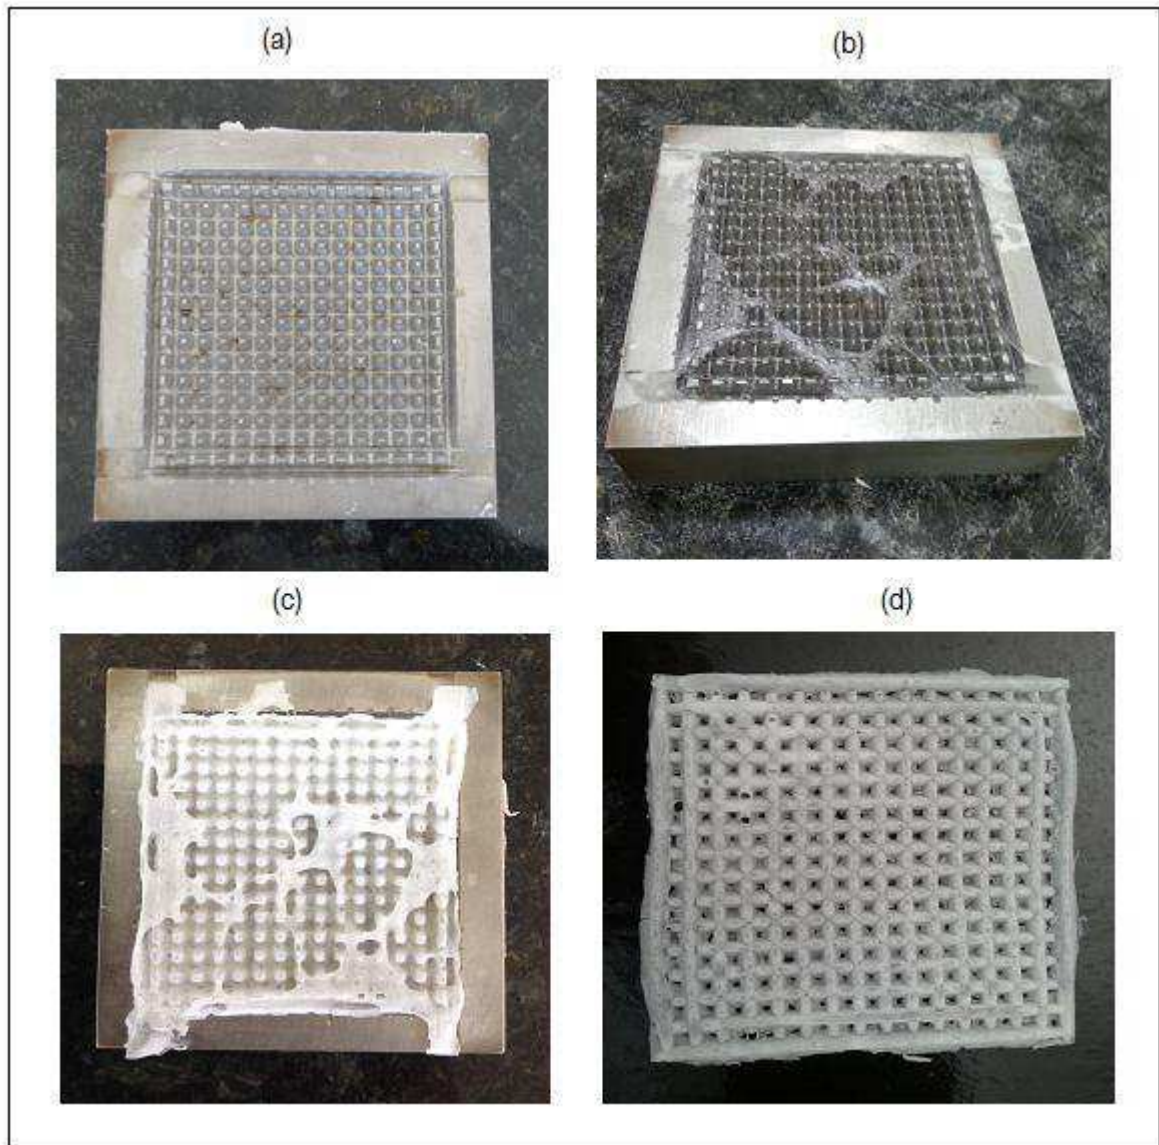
Confeção da tela de PCL, (a) Molde de Ferro, (b) Distribuição do PCL + solvente, (c) Secagem da tela no molde, (d) Tela pronta (Própria).
